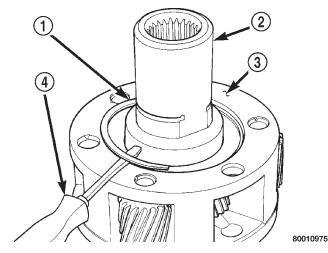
Desmontaje del anillo de muelle del engranaje impulsor
